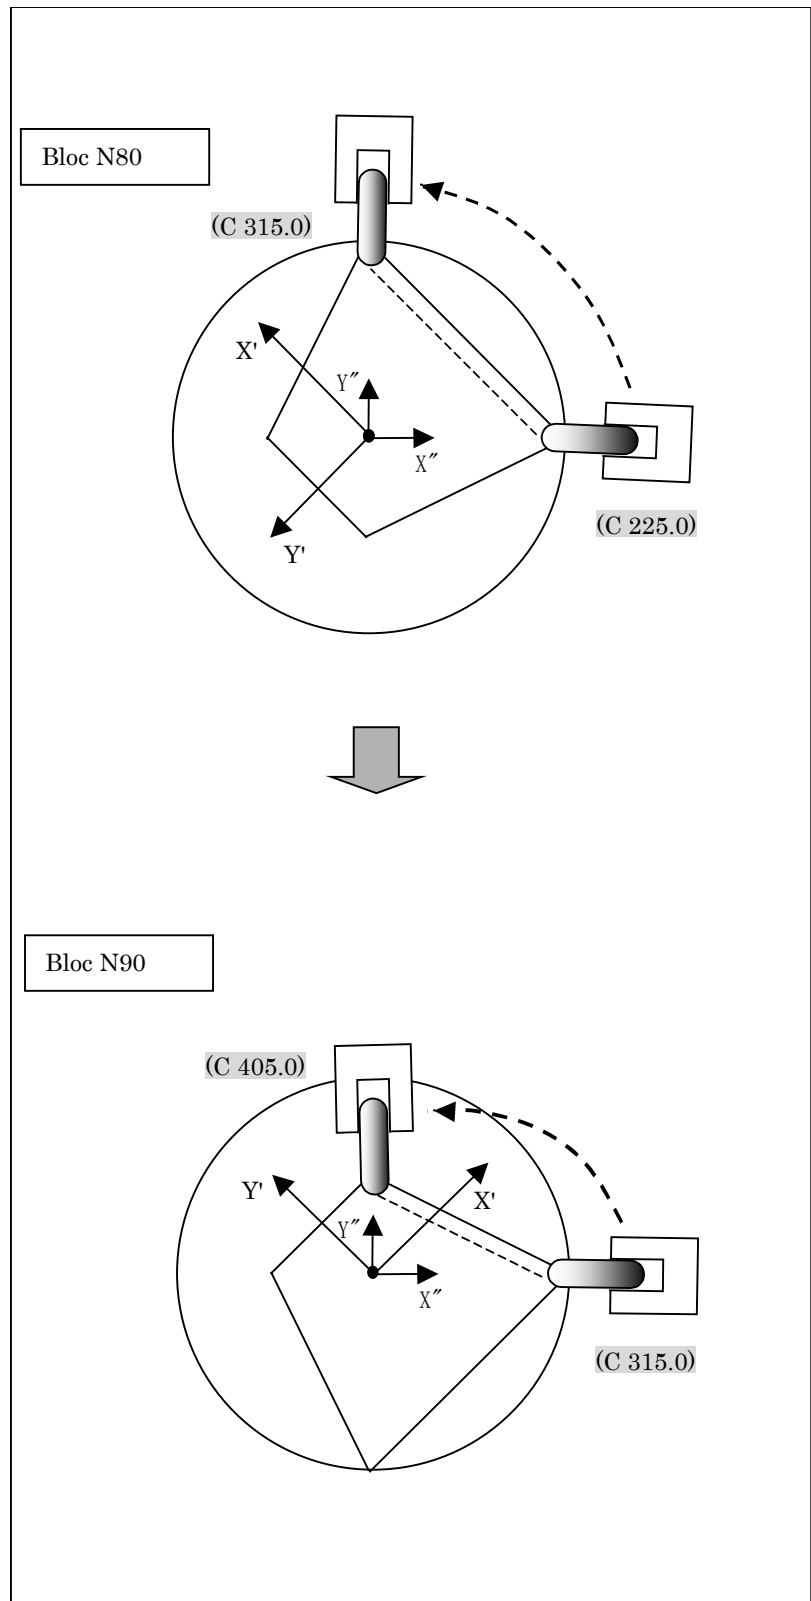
(d) Vue éclatée de chaque bloc (2)
